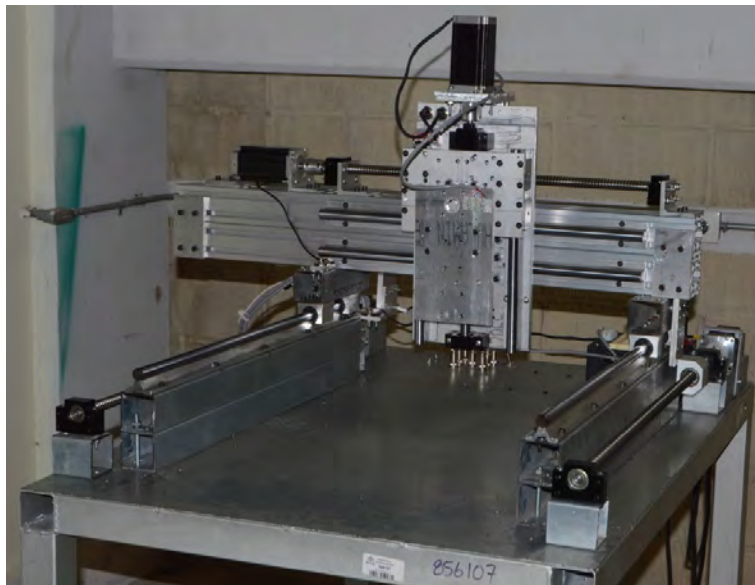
Máquina CNC montada sobre la mesa de trabajo.
